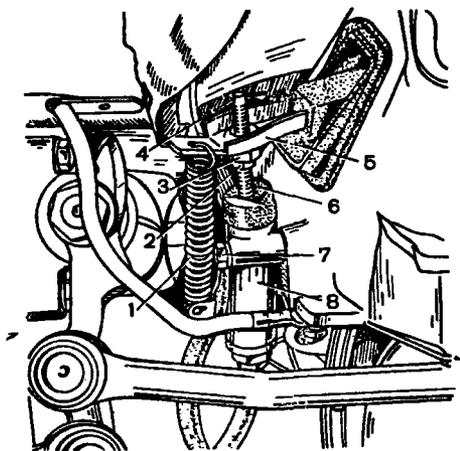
Привод выключения сцепления: 1 - оттяжная пружина вилки; 2 - контргайка; 3 - регулировочная гайка тяги; 4 - шплинт; 5 - вилка выключения сцепления; 6 - толкатель; 7 - болт крепления рабочего цилиндра к картеру сцепления; 8 - рабочий цилиндр привода выключения сцепления
